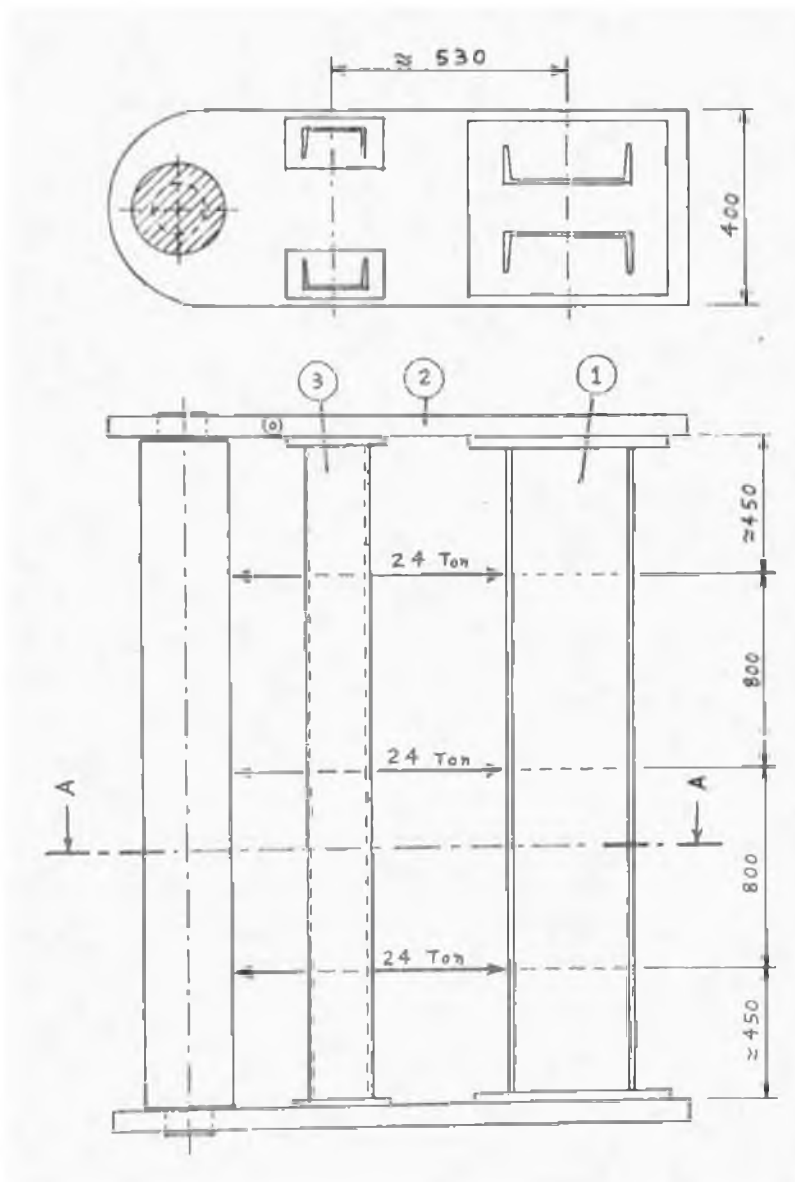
Composición del bastidor, dimensiones principales y cargas actuantes.
